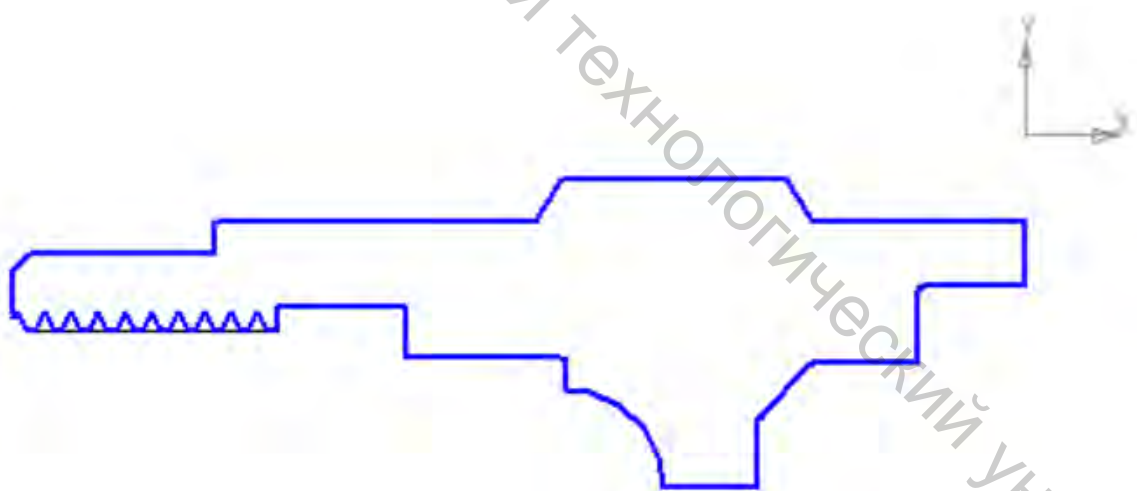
Фрагмент обработанной операционной заготовки
